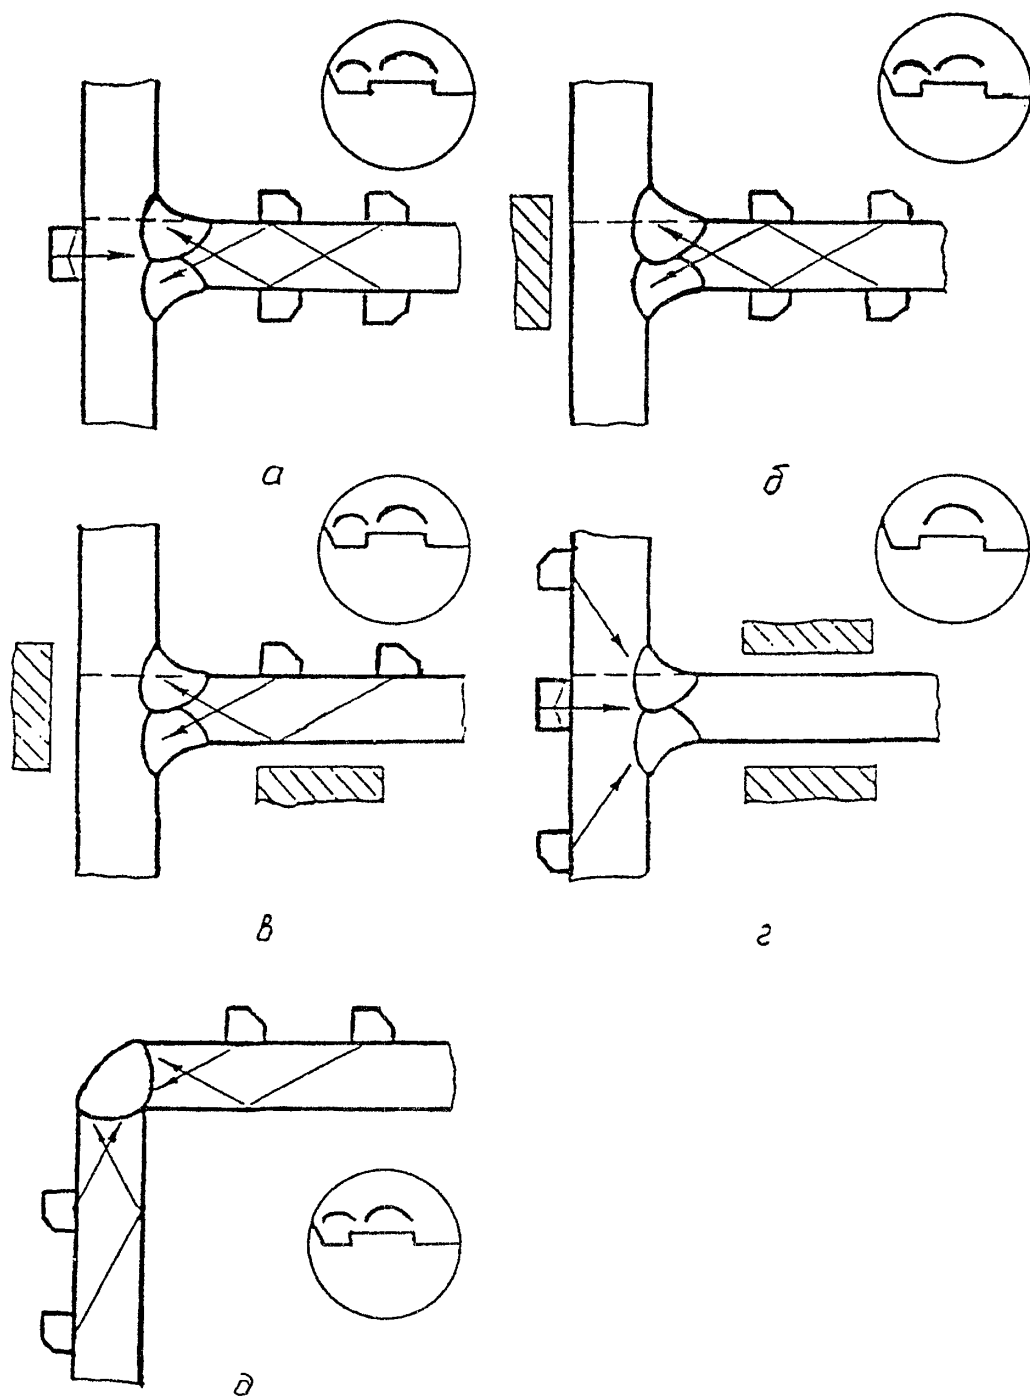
Схемы контроля угловых и тавровых сварных соединений, выполненных без конструктивных непроваров.
